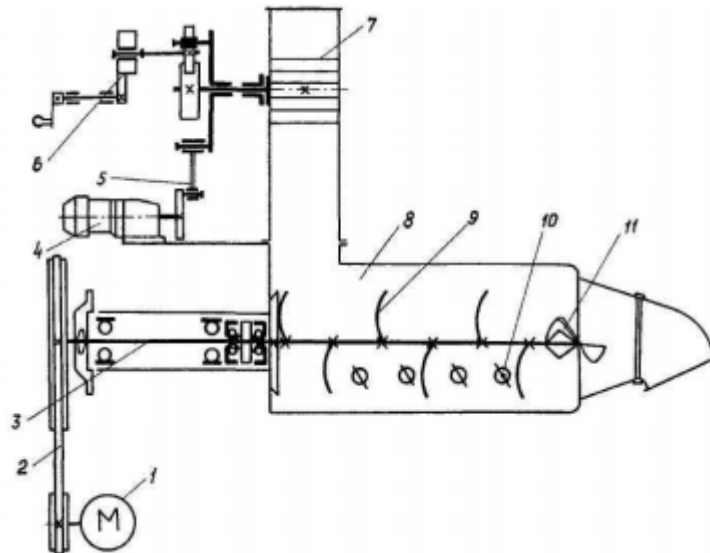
Кінематична схема машини тістомісильної ЦАИГХТК: 1 - електродвигун; 2 - клинопасова передача; 3 - місильний вал з лопатями; 4 - редуктор; 5 - шатун; 6 - механізм регулювання продуктивності; 7 - роторний дозатор борошна; 8 - місильна камера; 9 - лопать; 10 - гальмівна лопать; 11 – пластифікатор
